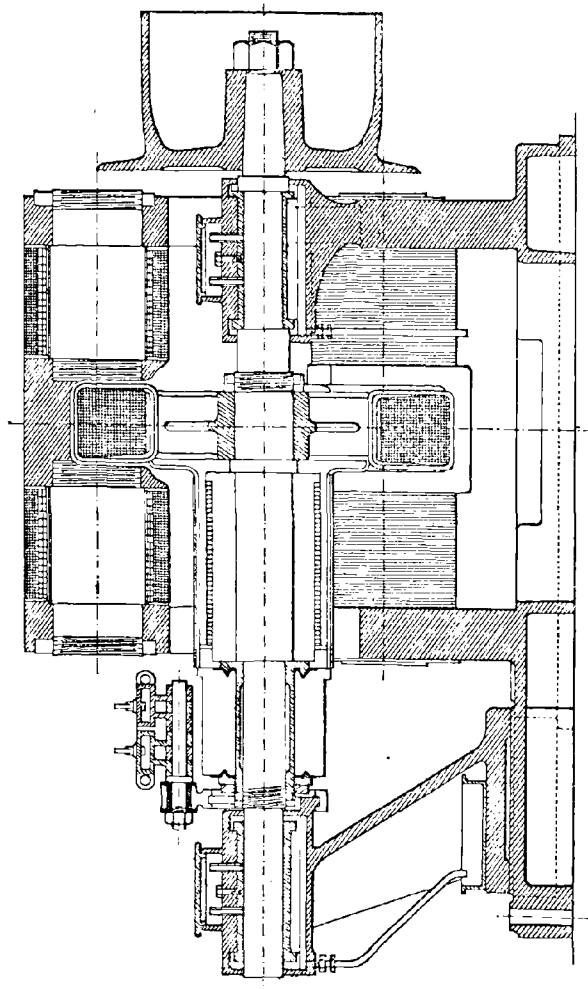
Machine Gülcher (1888). — Coupe en long.
